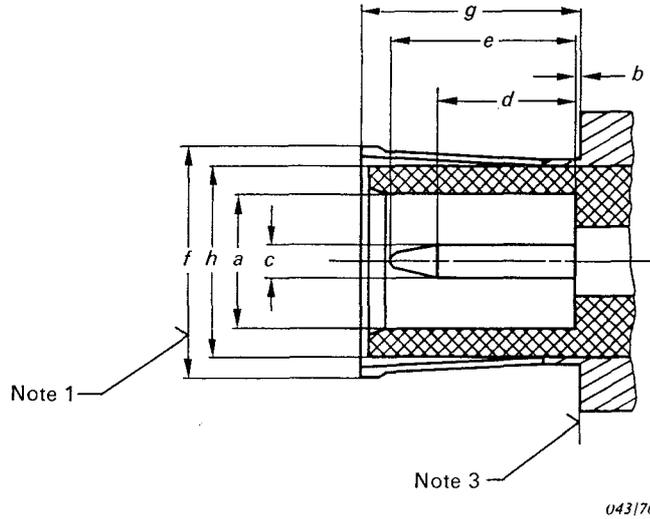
Connecteur mâle (dimensions, voir le tableau).
